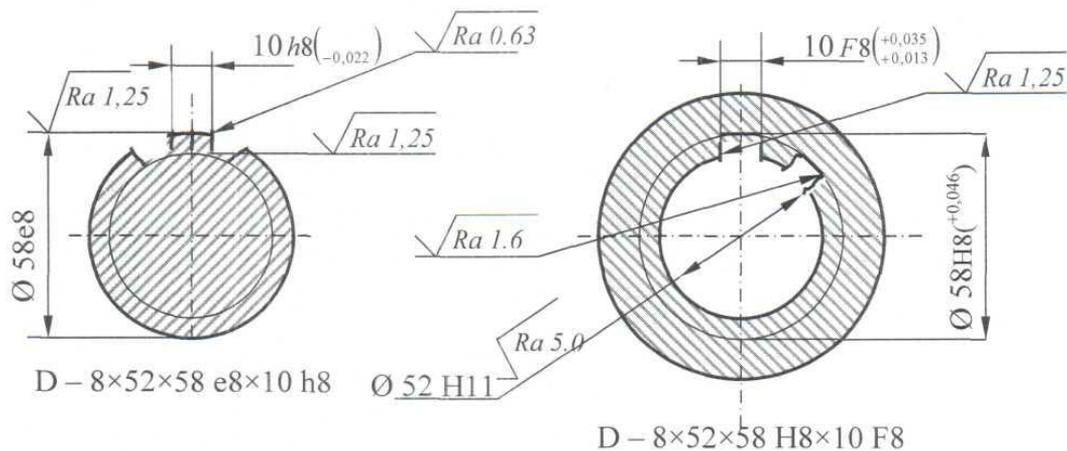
Обозначение допусков и предельных отклонений на рабочих чертежах деталей шлицевого соединения
